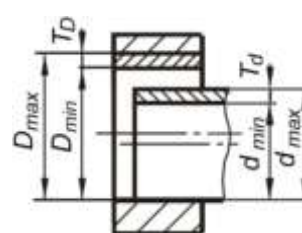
Графическое изображение полей допусков отверстия и вала
